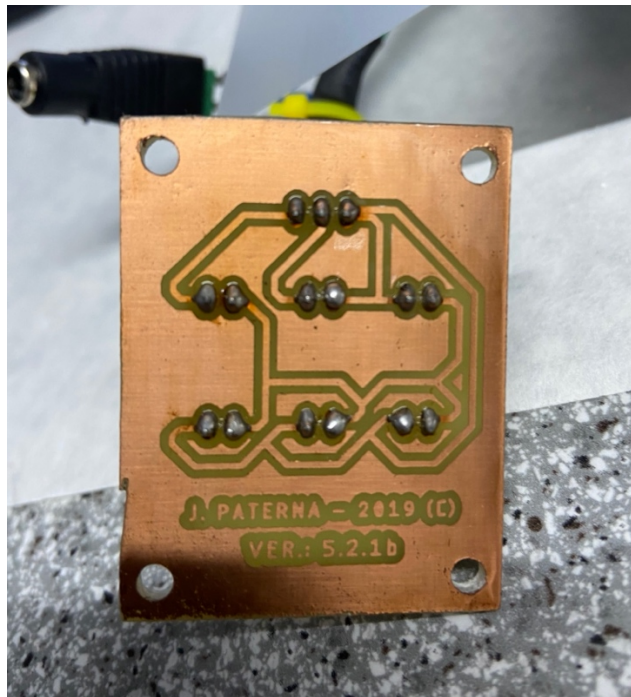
B. Imagen de la PCB fabricada para las conexiones del dispositivo. (fotografía realizada por J. Paterna).
